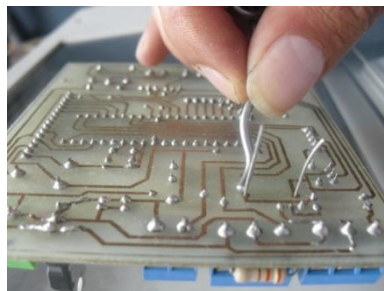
F TERMINADO DEL SOLDADO DE COMPONENTES
